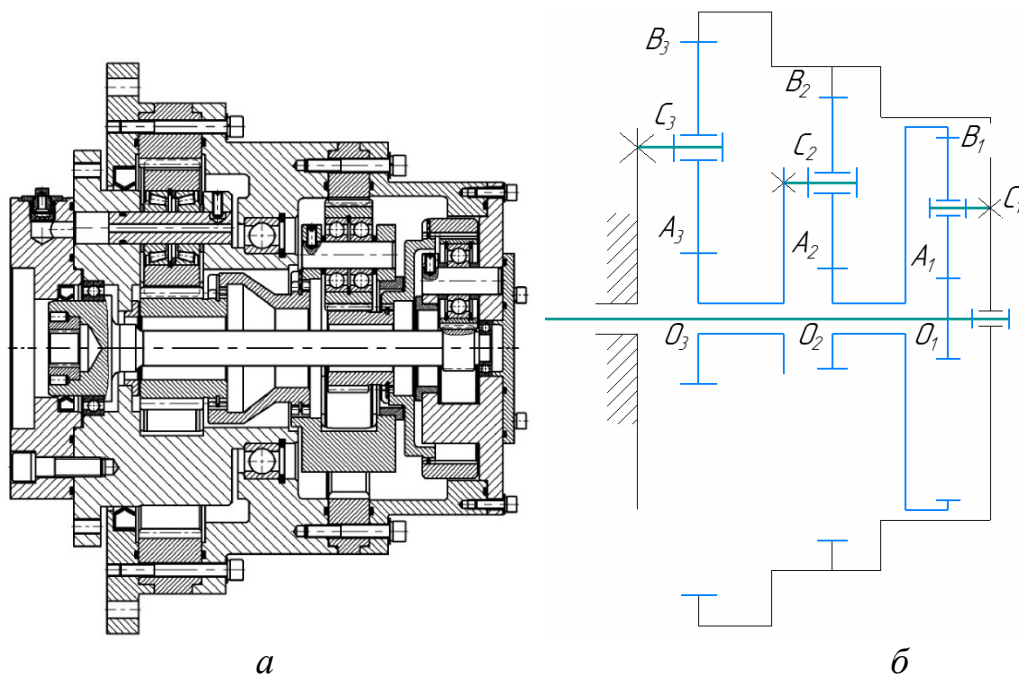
Планетарная передача, встраиваемая в барабан механизма подъема башенного крана: *а* - разрез планетарного трехступенчатого редуктора; *б* - кинематическая схема
